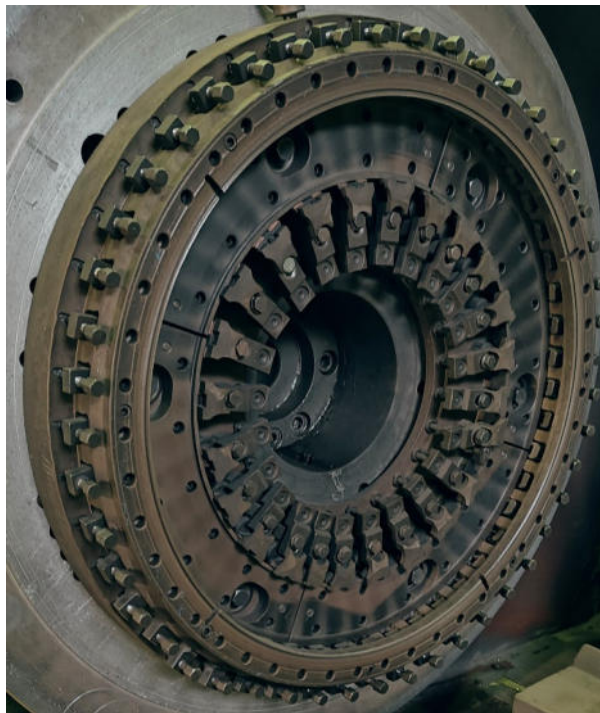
Общий вид роторного приспособления, установленного на токарно-лобовом станке необходимого для шлифования сопловых лопаток
